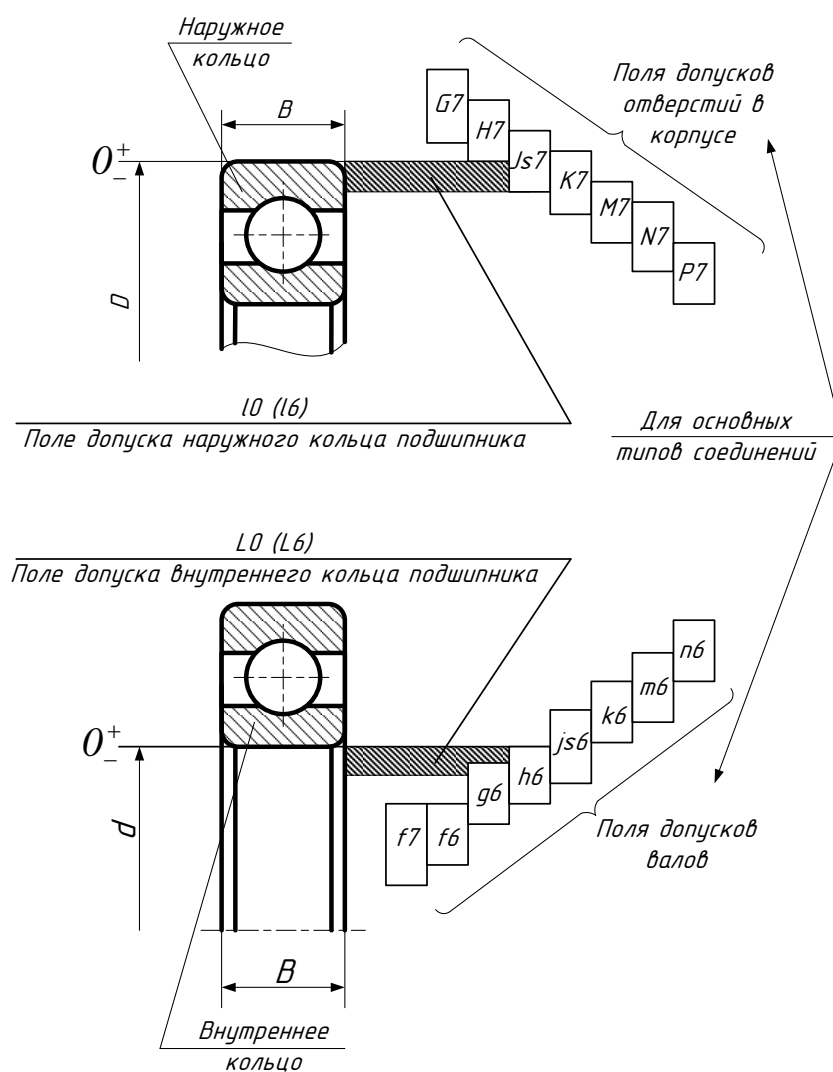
Поля допусков посадочных поверхностей подшипников, отверстий и валов для установки подшипников качения 0 и 6 классов точности
